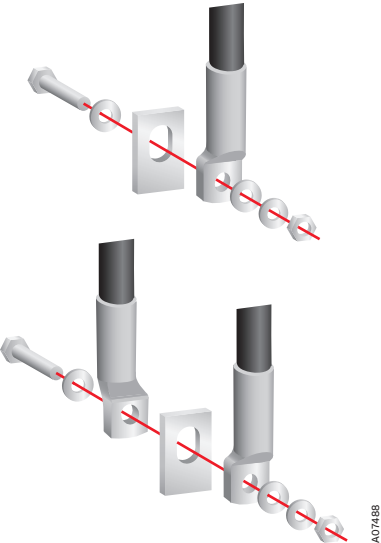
OX_30-800, kabeldragning med kabelskor
